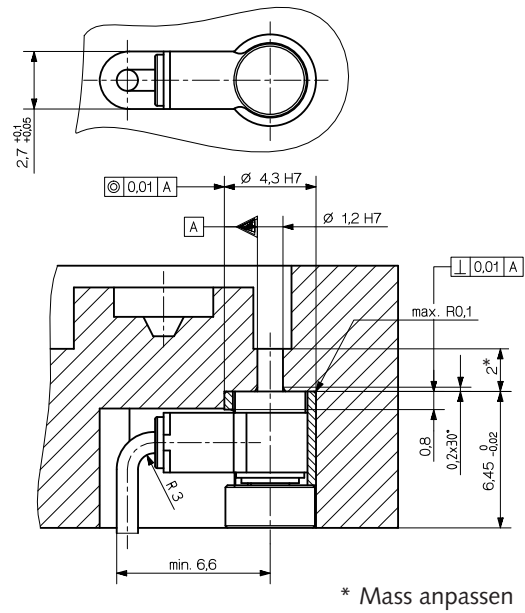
Einbau mit Distanzhülse Typ 6466 und Druckscheibe Typ 6470
